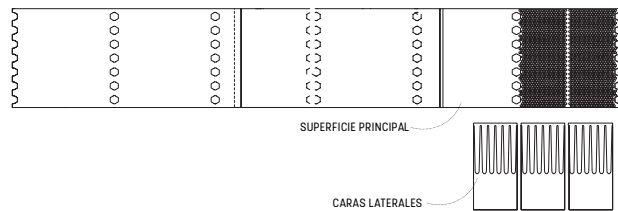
Desarrollo para corte láser de prototipo en estireno.
